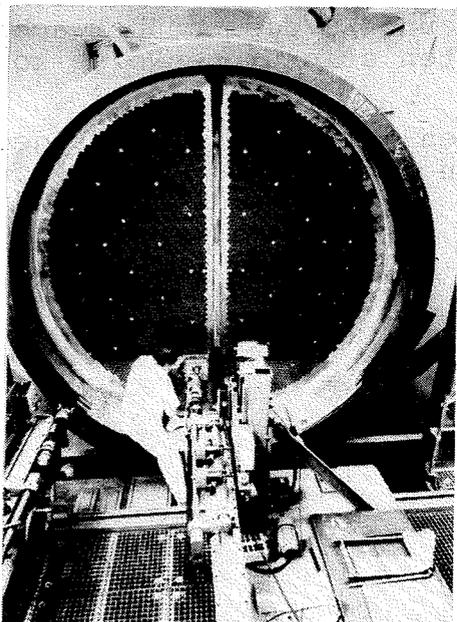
Arbeitsprobe zur Rohreinschweißung beim Dampferzeuger (Werk-Foto MAN-GHH Sterkrade)
